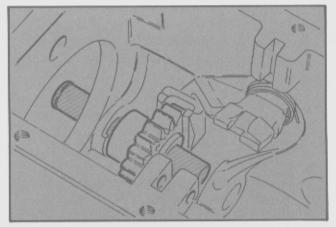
Instalación del engranaje intermediario de retroceso.
